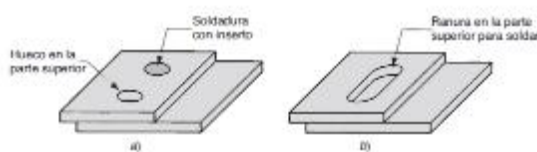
a) Soldadura de muesca. b) Soldadura de tapón.
